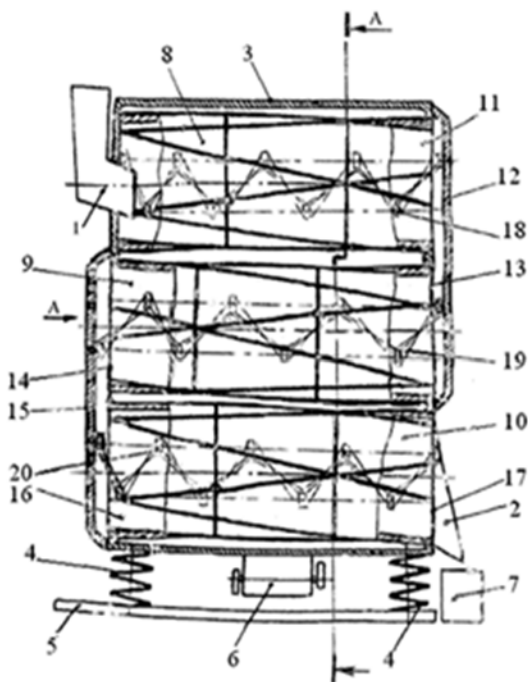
Вибрационная малогабаритная установка для приготовления кормов:
